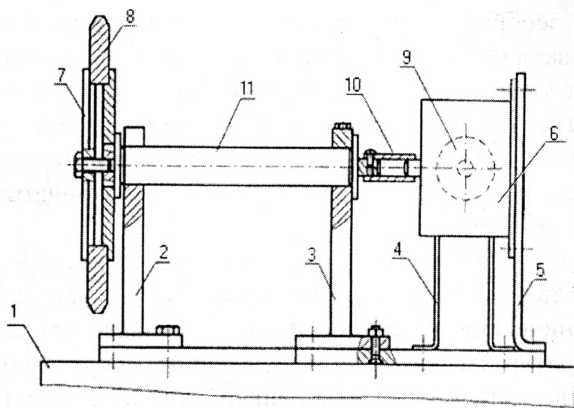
Привод вращения диска в процессе термической обработки: 1 — стол; 2 – 5 — опоры; 6 — редуктор; 7 — механизм крепления; 8 — диск; 9 — двигатель; 10 — соединительная муфта; 11 — вал
